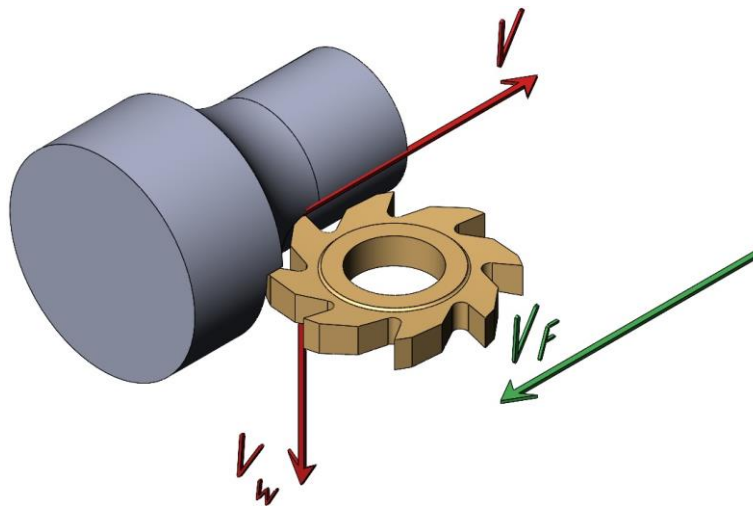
Высокоскоростное плунжерное фрезерование дисковой фрезой
